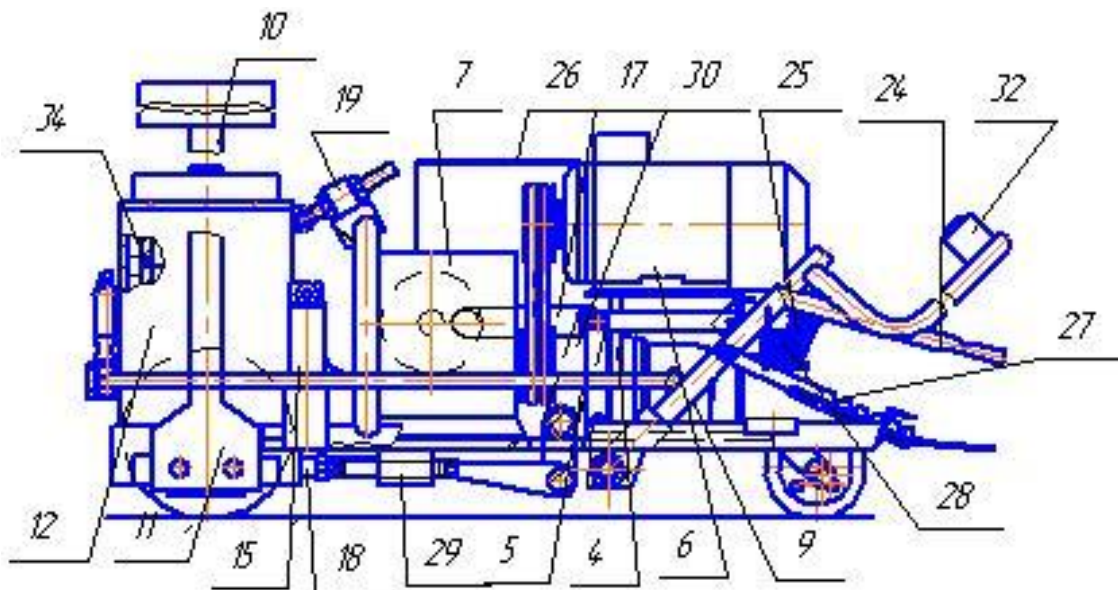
Устройство для выпрессовки шкворней.
